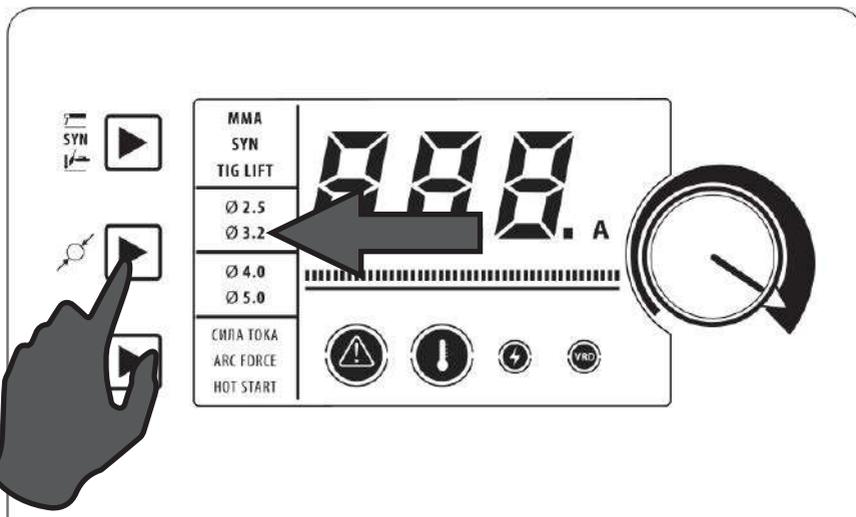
Выбор диаметра сварочного электрода.
